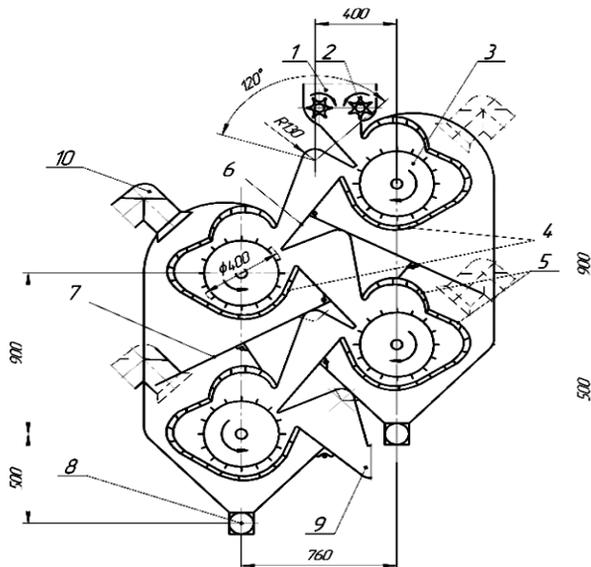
Четырехбарабанный очиститель (опытный образец)
